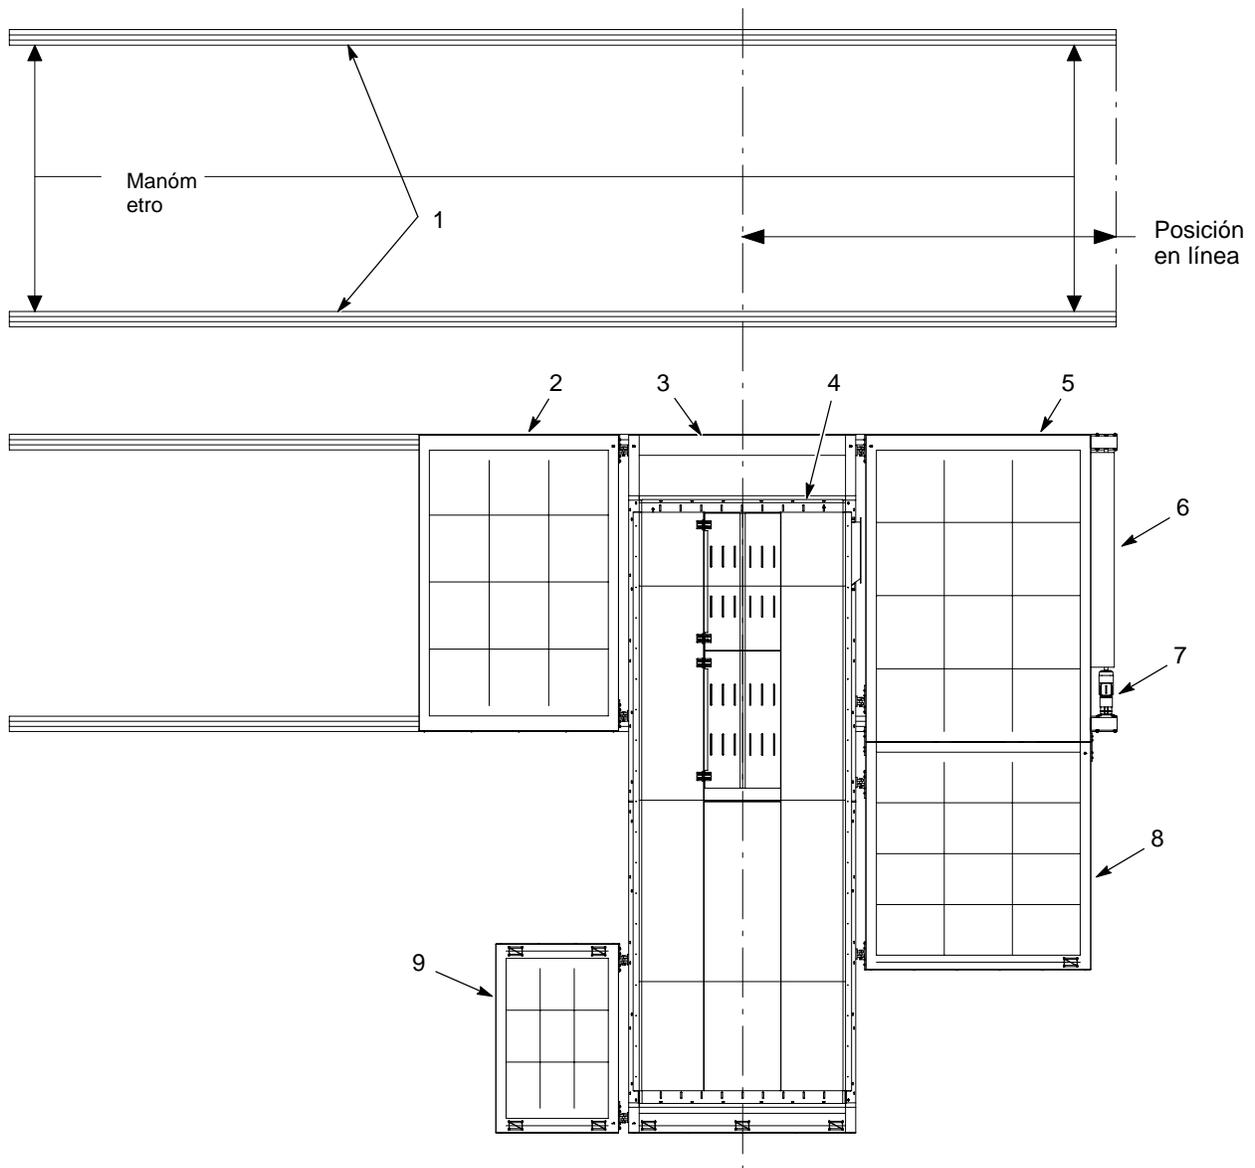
Instalación de la base, cabina de enrollado/desenrollado (típico)
